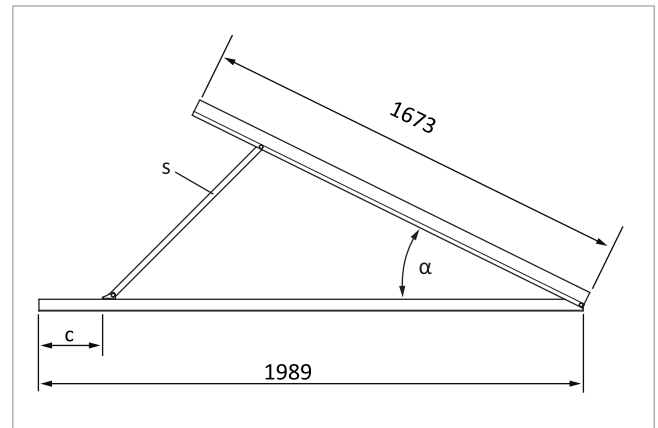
Soporte para tejado plano, dimensiones y ángulo de colocación
